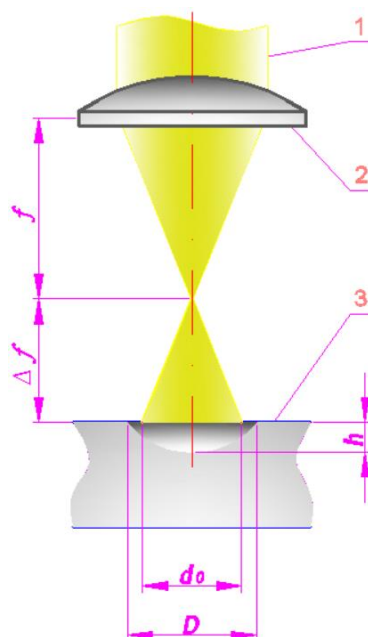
Схема фокусування проміння: 1 – лазерний пучок; 2 – лінза; 3 – заготовка
